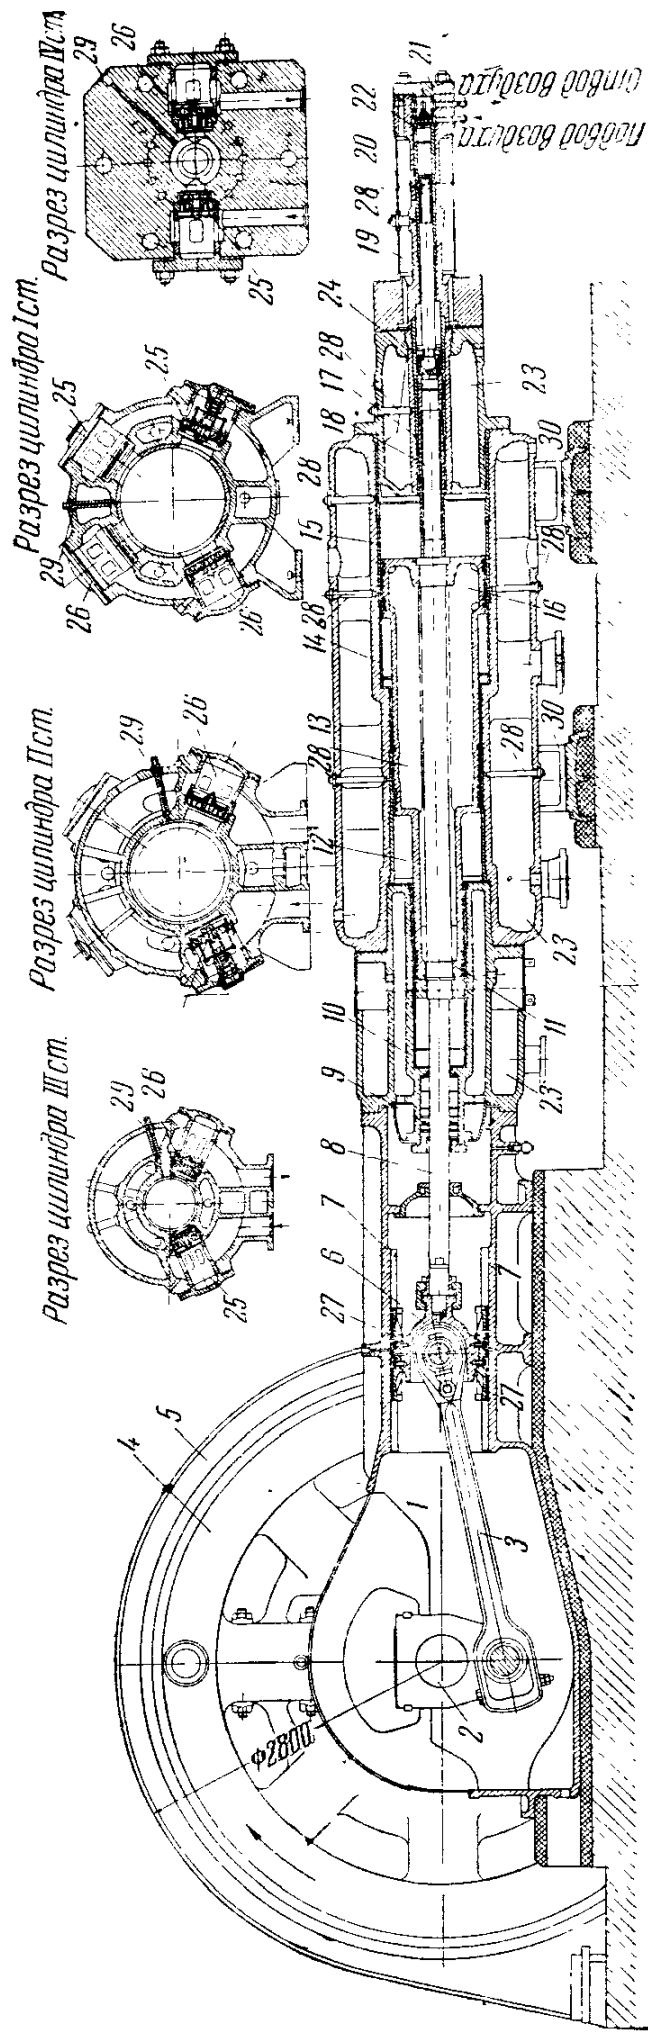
Разрезы компрессора типа 5Э-14/220:
